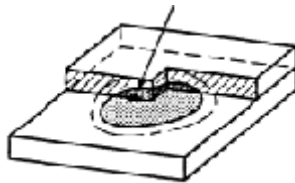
Representação de inclusões no ponto de soldadura
